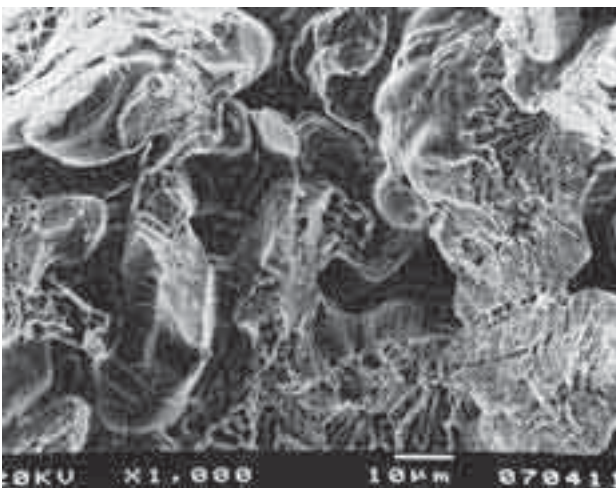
MEV da fratura interdendrítica no corpo-de-prova na condição soldado por brasagem; 1000X.
